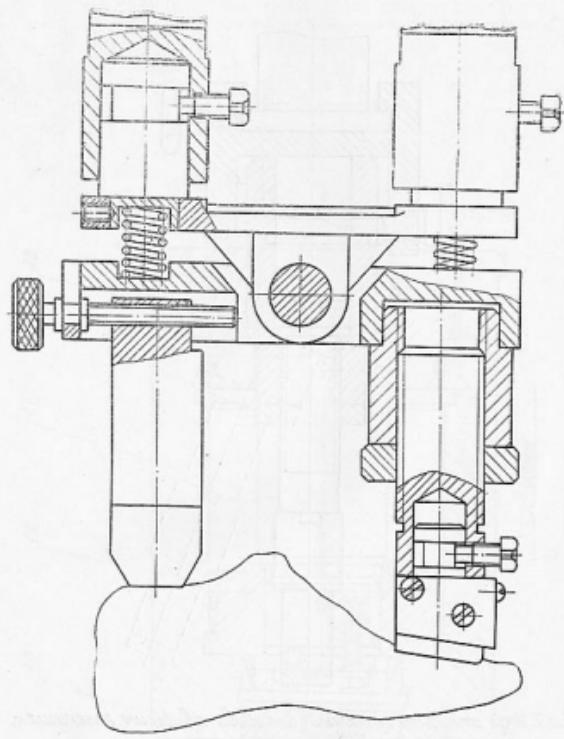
Упор гусеничный для гусениковой и малобортовой обуви.
